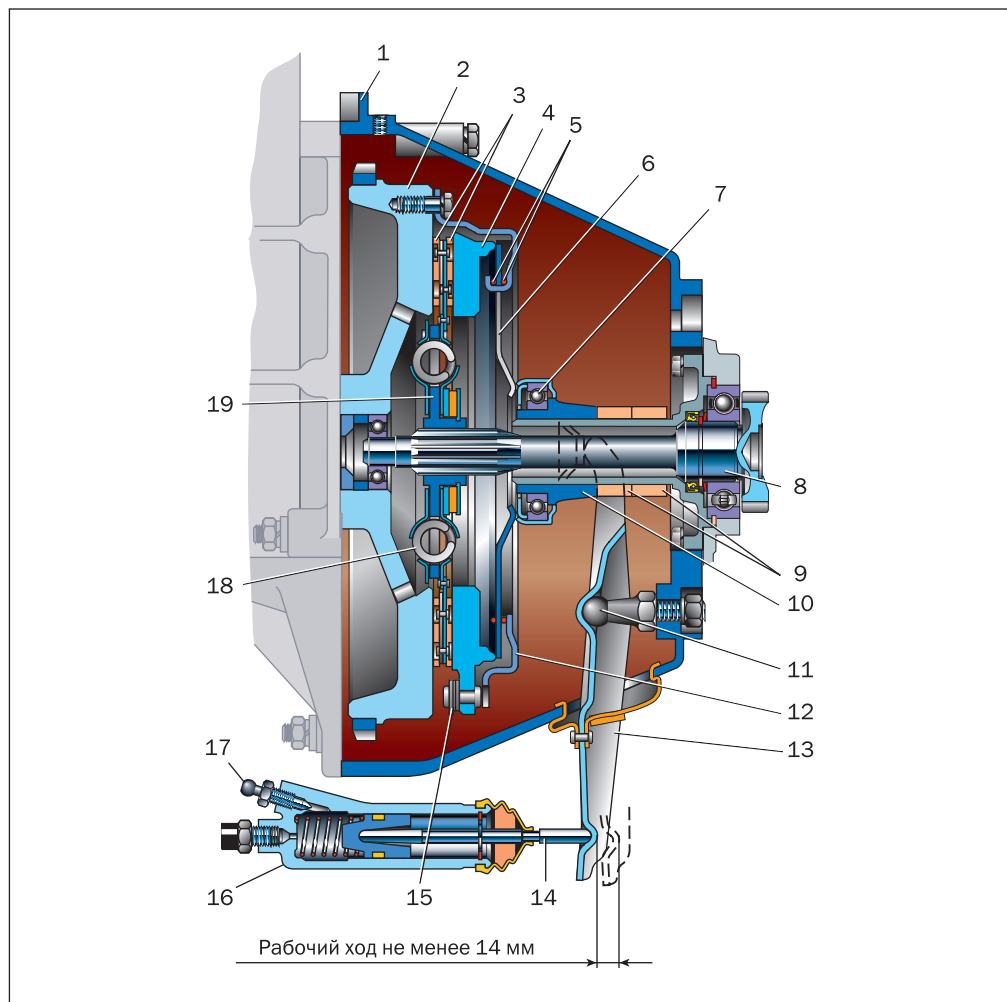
Однодисковое сцепление: 1 — картер сцепления; 2 — маховик; 3 — фрикционные накладки ведомого диска; 4 — нажимной диск; 5 — опорные кольца; 6 — диафрагменная пружина; 7 — подшипник выключения сцепления; 8 — первичный вал коробки передач; 9 — поролоновые кольца; 10 — муфта выключения; 11 — шаровая опора вилки; 12 — кожух; 13 — вилка; 14 — шток рабочего цилиндра; 15 — соединительная пластина; 16 — рабочий цилиндр; 17 — штуцер прокачки; 18 — демпферная пружина; 19 — ступица ведомого диска
